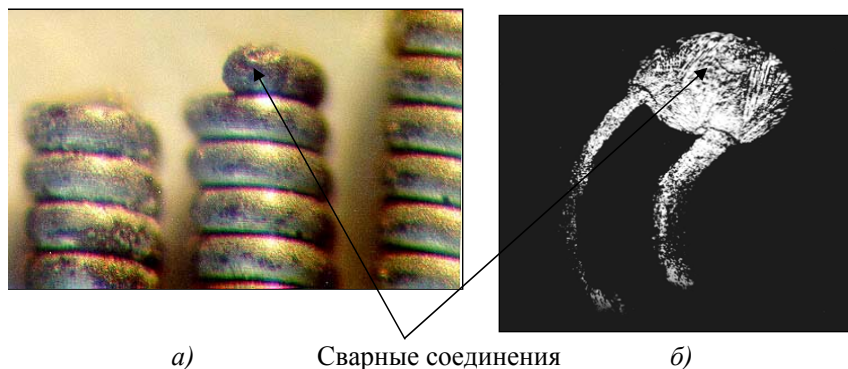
Внешний вид (а) и сечение (б) сварного соединения торца капсулы источника на основе церия-144. Материал корпуса – сталь 12Х18Н10Т
